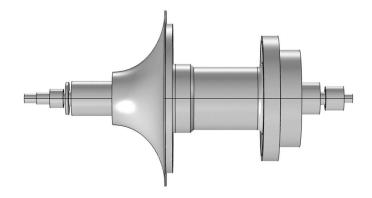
Турбокомпрессор с подшипниками, расположенными в крайних частях вала.
